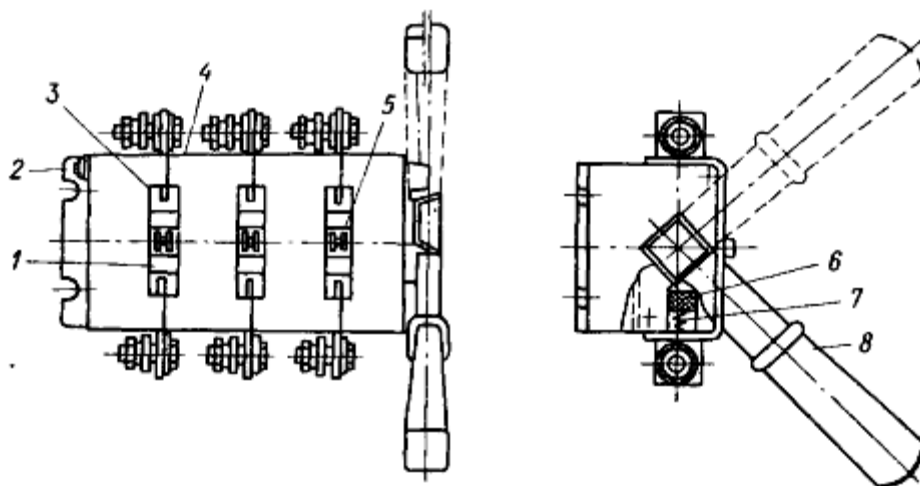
Загальний вид трьохполюсного рубильника серії Р
